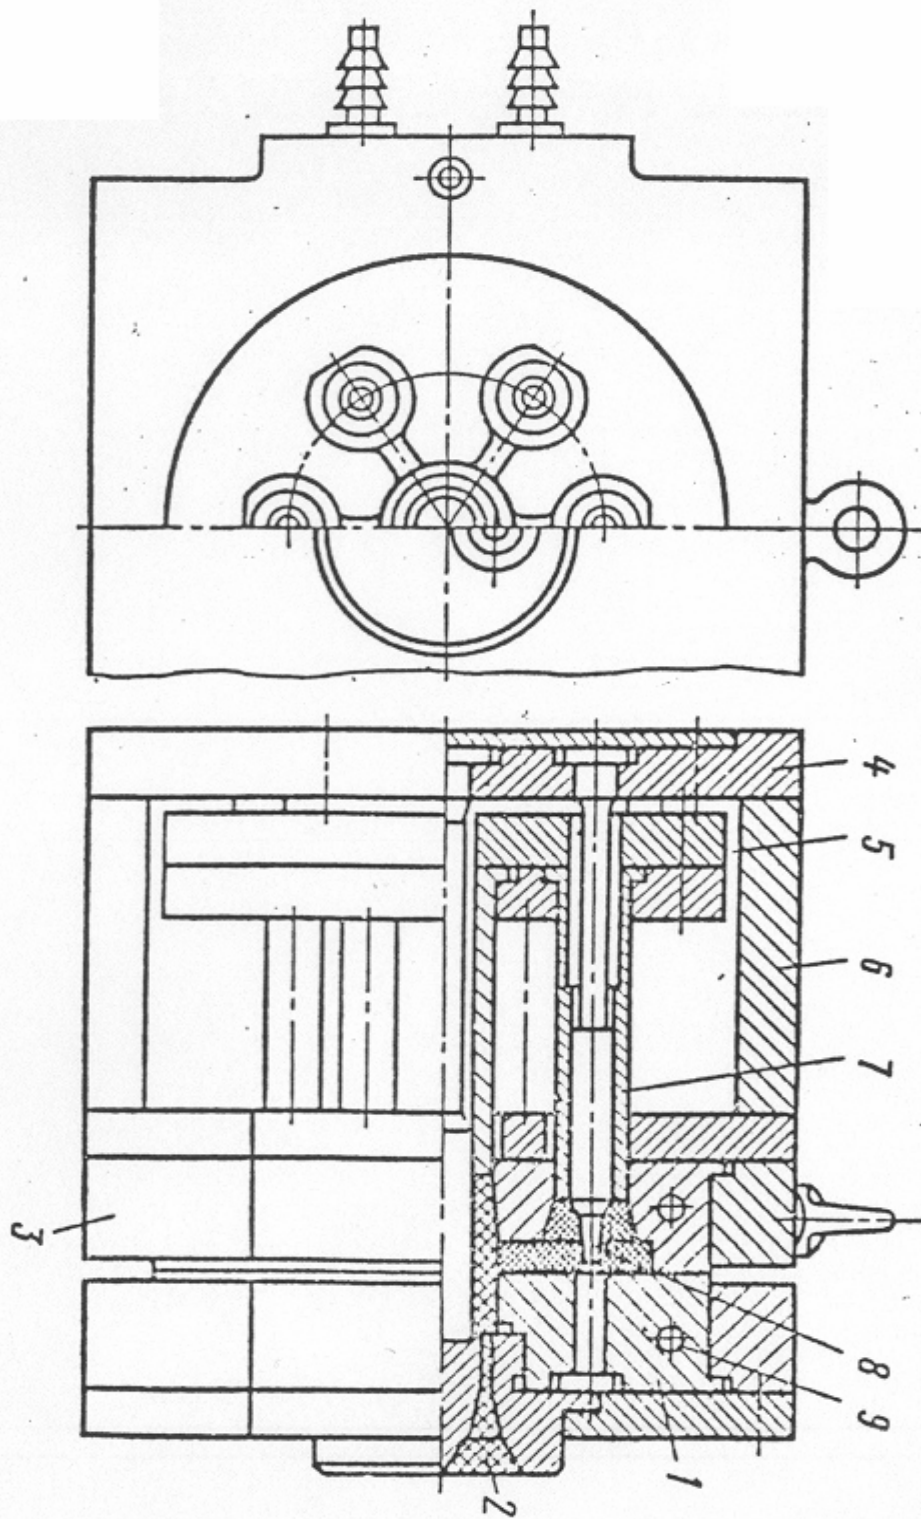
Пресс-форма для изготовления моделей в массовом производстве: 1 – подвижная матрица; 2 – канал для подачи модельного состава; 3 – неподвижная матрица; 4 – плита выталкивателей; 5 – плита стержней; 6 – стойки; 7 – трубчатые толкатели; 8 – стержни; 9 – каналы системы термостатирования пресс-формы.
